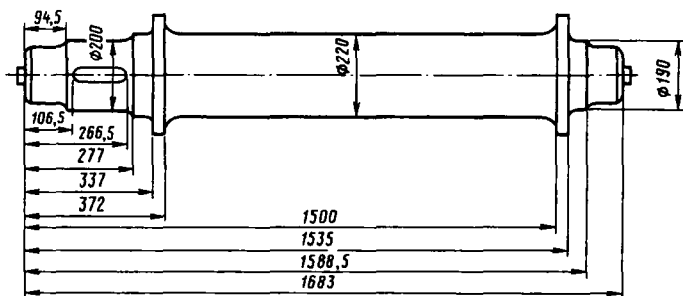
Главный приводной вал эскалатора ЭТ-5М
